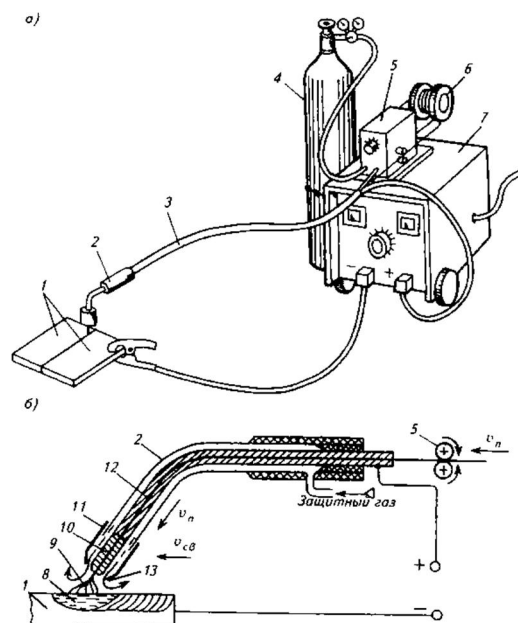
Устаткування (а) і схема напівавтоматичного зварювання в захисному газі (б)
